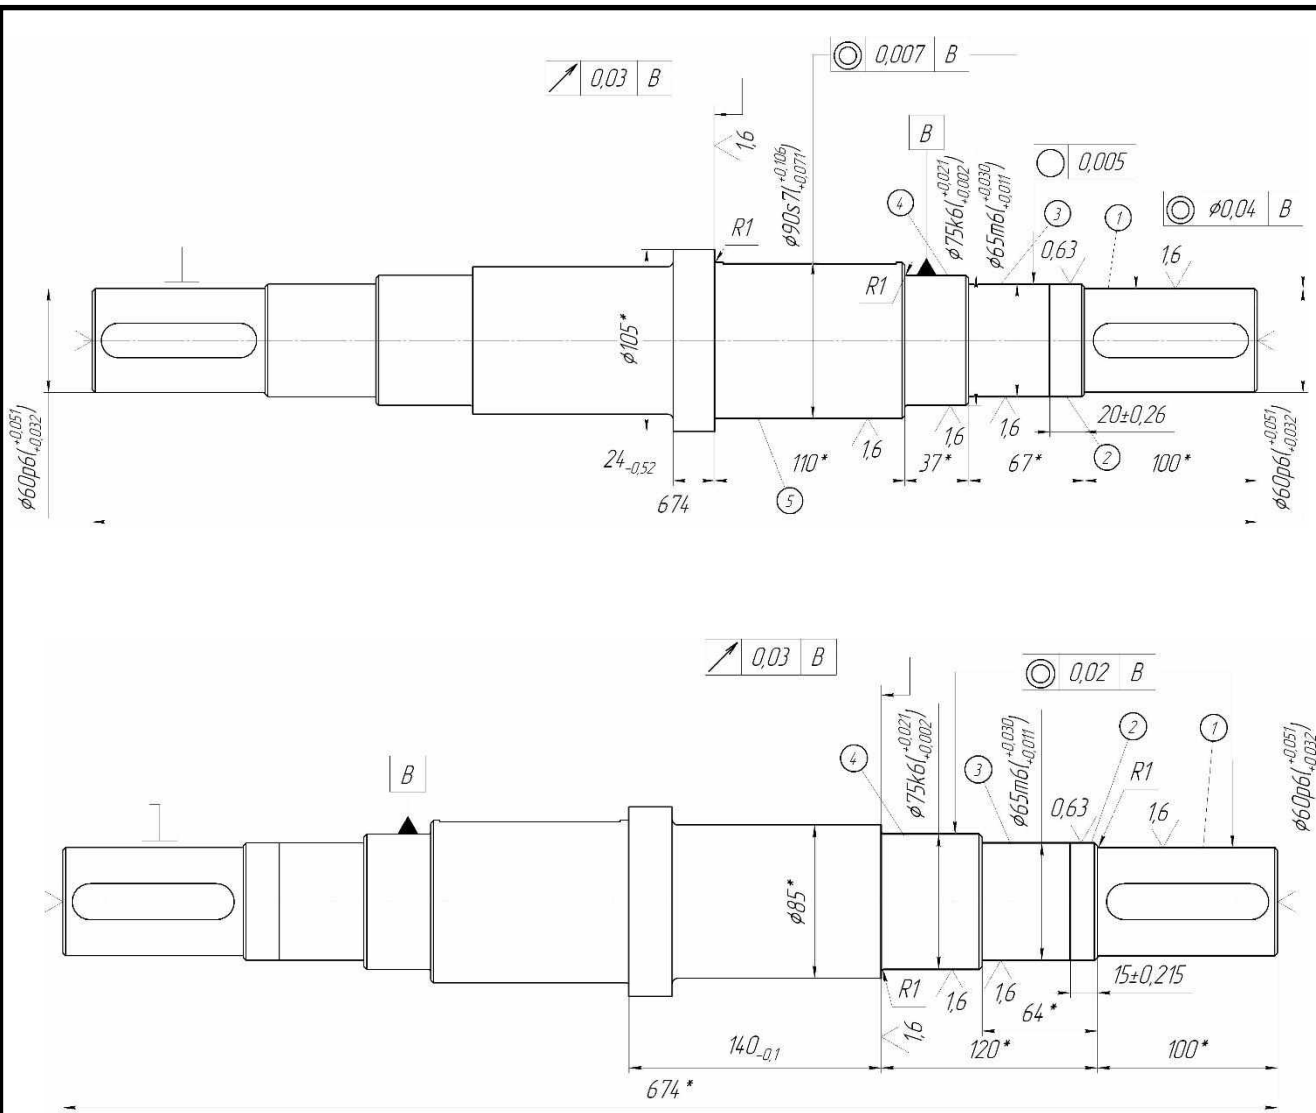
Ескізи обробки деталі, операції 060Б та 060А
